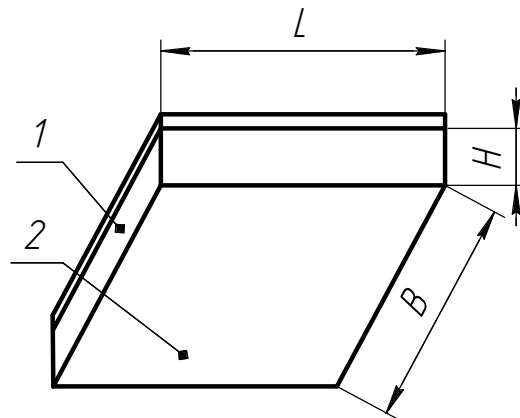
ЛПО46-4x18; 1. Корпус в сборе, 2. Рассеиватель
